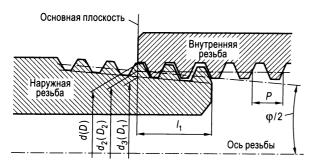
Соединение наружной конической резьбы с внутренней цилиндрической резьбой
